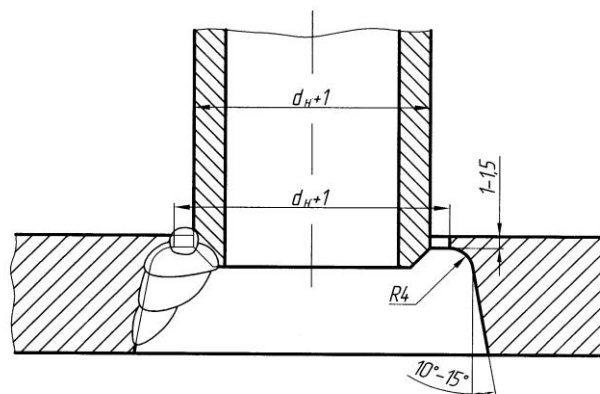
Сборка и сварка соединения трубок с нижней трубной решеткой
